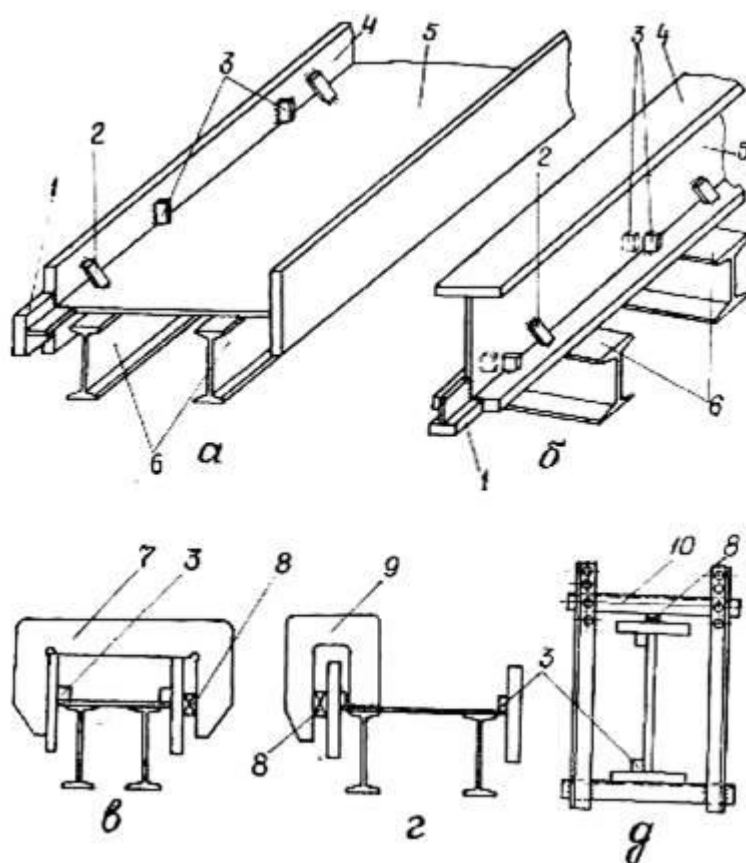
Сборка балок составного двутаврового сечения по разметке: а -- сборка в горизонтальном положении; б -- сборка в вертикальном положении; в -- стягивание листов сечения объемлющей скобой; г -- стягивание листов сечения односторонней сборочной скобой; д -- стягивание листов сечения хомутом; 1 -- выводные планки; 2 -- наклонные соединительные планки; 3 -- временные упоры; 4 -- горизонтальные листы (полки); 5 -- вертикальный лист (стенка); 6 -- прокатные балки стеллажа; 7 -- объемлющая сборочная скоба; 8 -- сборочный клин; 9 -- односторонняя сборочная скоба; 10 -- сборочный хомут.
